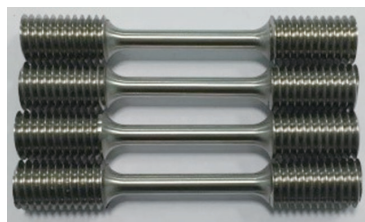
GH3230 高温合金 TLP 扩散对接焊缝拉伸试样
